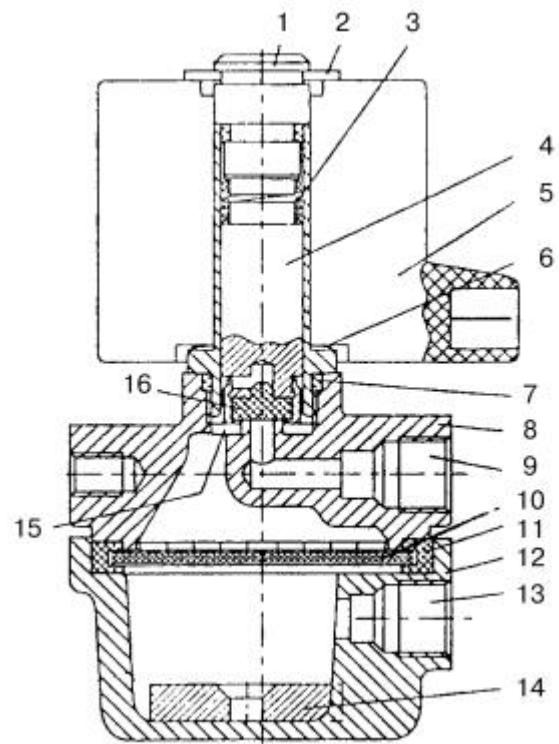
Электромагнитный газовый клапан: 1 – направляющая втулка; 2, 6 – стопорное кольцо; 3 – пружина; 4 – якорь; 5 – катушка; 7 – уплотнитель; 8 – корпус; 9 – входной канал; 10 – металлическая обойма с фильтром; 11 – резиновое кольцо; 12 – отстойник; 13 – выходной канал; 14 – постоянный кольцевой магнит; 15 – кольцевая полость; 16 – уплотнитель.
